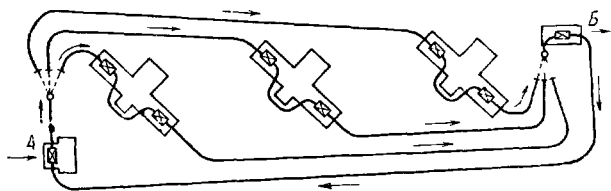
Монорельсовый путь для подачи деталей к станкам
